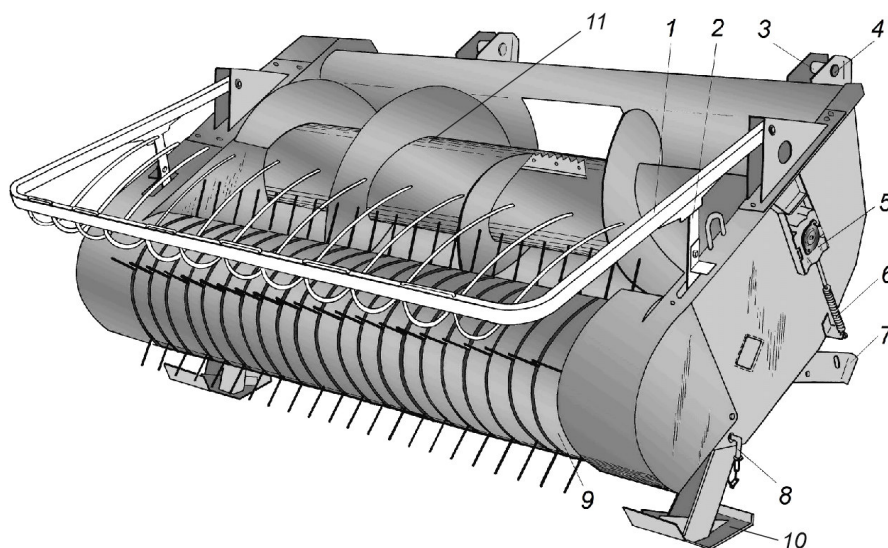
Подборщик: 1 – прижимное приспособление; 2 – стойка; 3 – верхний ловитель; 4 – ось; 5 – опоры шнека; 6 – пружины; 7 – нижний ловитель; 8 – фиксатор; 9 – подбирающий барабан; 10 – башмак; 11 – шнек
